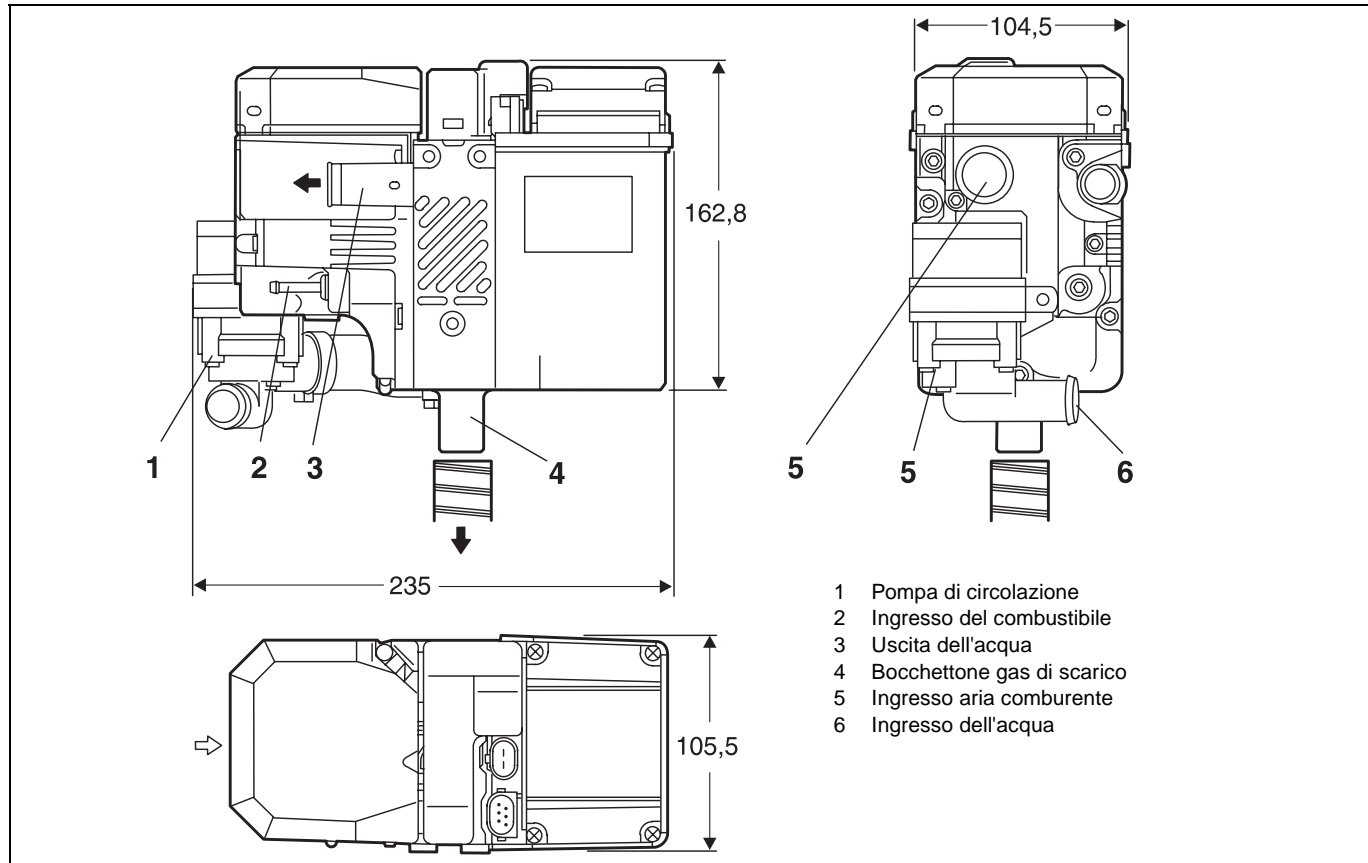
Disegno di montaggio Thermo Top E e Z/C
